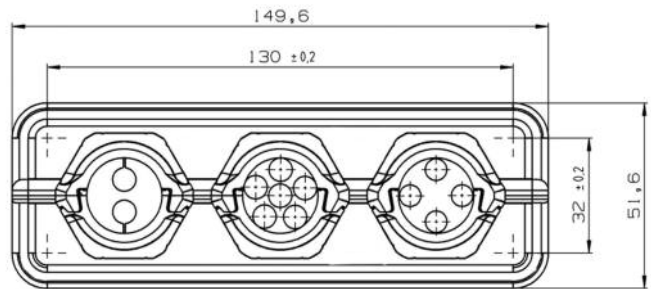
Maße des UNI FLANSCH™ mit Gewindeeinsätzen (Artikel-Nummer: UFLG3)
